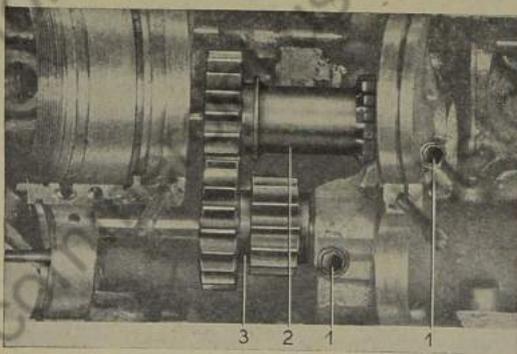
Schieberäder für Rückwärts- und Geländegang ausbauen
